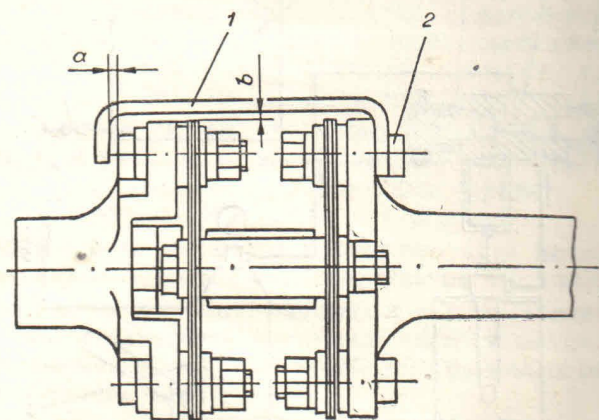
Центровка топливного насоса высокого давления с валом привода:
